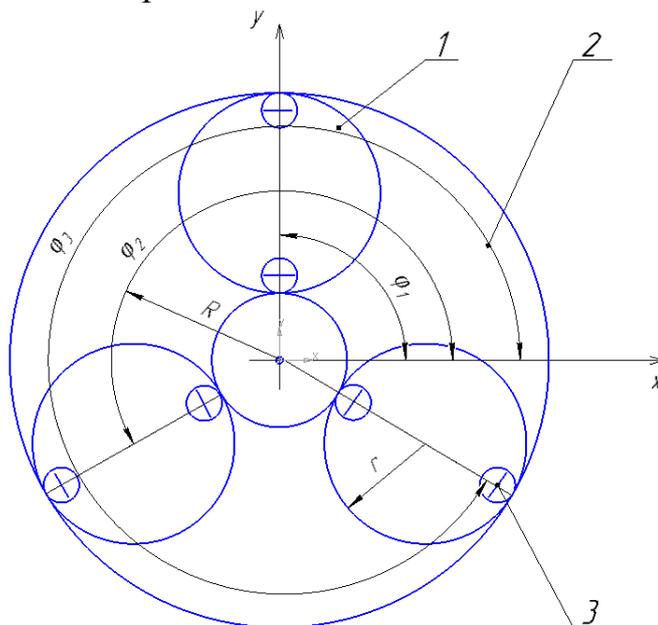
Схема планетарного ударно-скалывающего исполнительного органа
